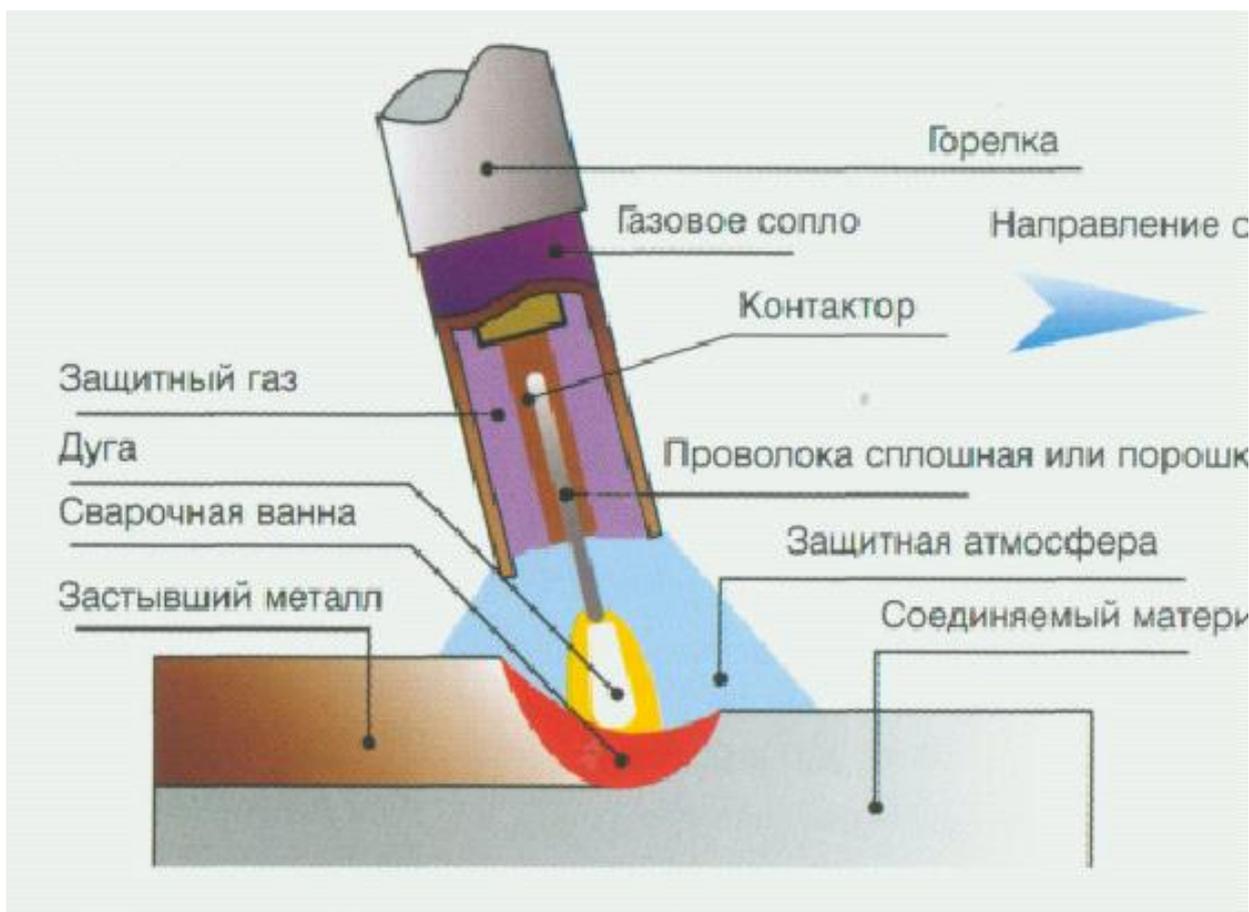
Схема полуавтоматической сварки в среде защитных газов
